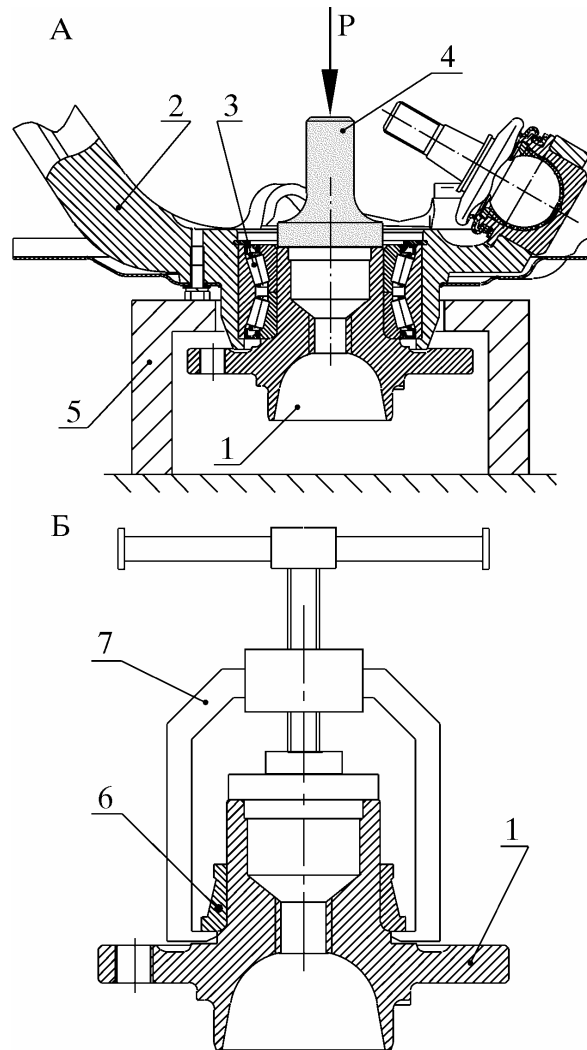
Выпрессовка ступицы колеса из подшипника поворотной стойки и спрессовка внутреннего кольца подшипника со ступицы:
